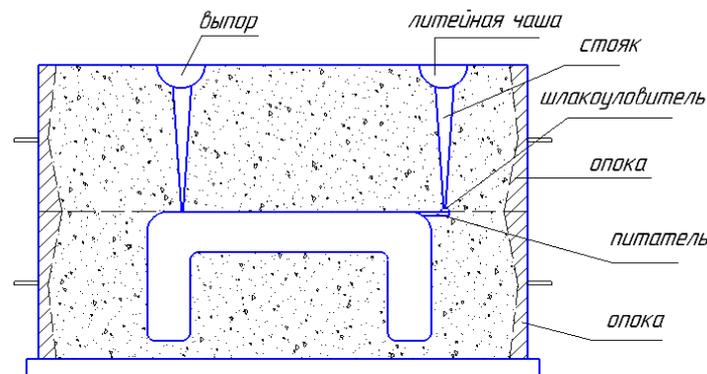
Литейная форма для получения отливок в песчаных формах
